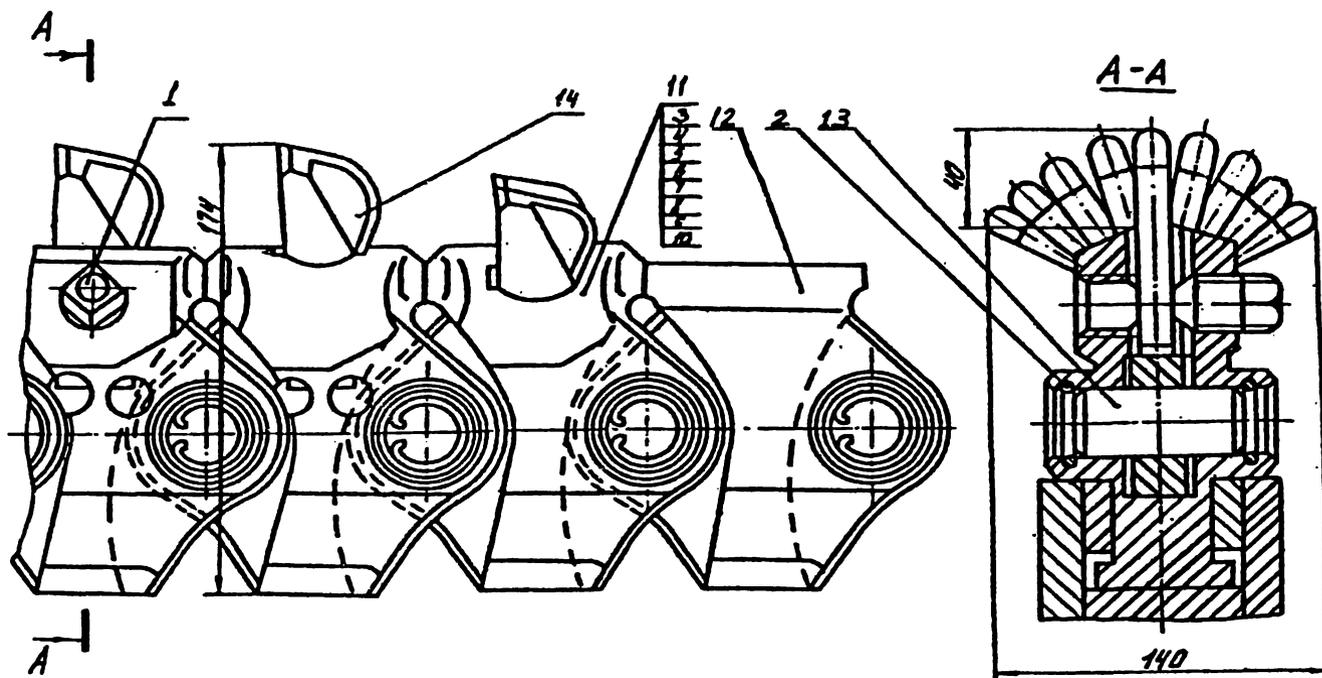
Режущая цепь комбайна «Урал-50»: 1 – стопор; 2 – кольцо пружинное; 3 – 11 – кулак; 12 – кулак промежуточный; 13 – палец; 14 – резец
